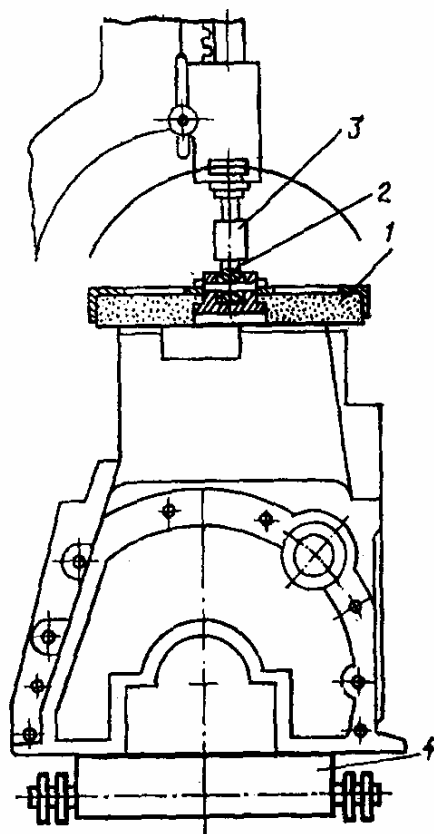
Пристрій для шліфування привалкової поверхні блока циліндрів на свердлильному верстаті:
